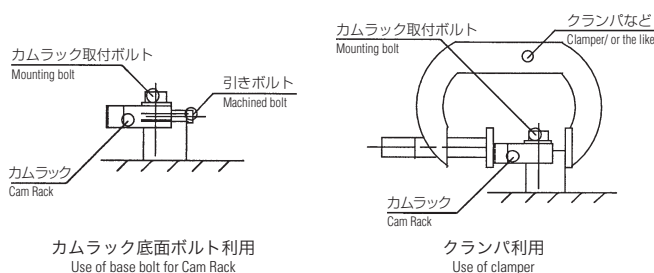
カムラック平行出し方法 Fig. 1 - Setting procedures for parallelism of Cam Rack -
